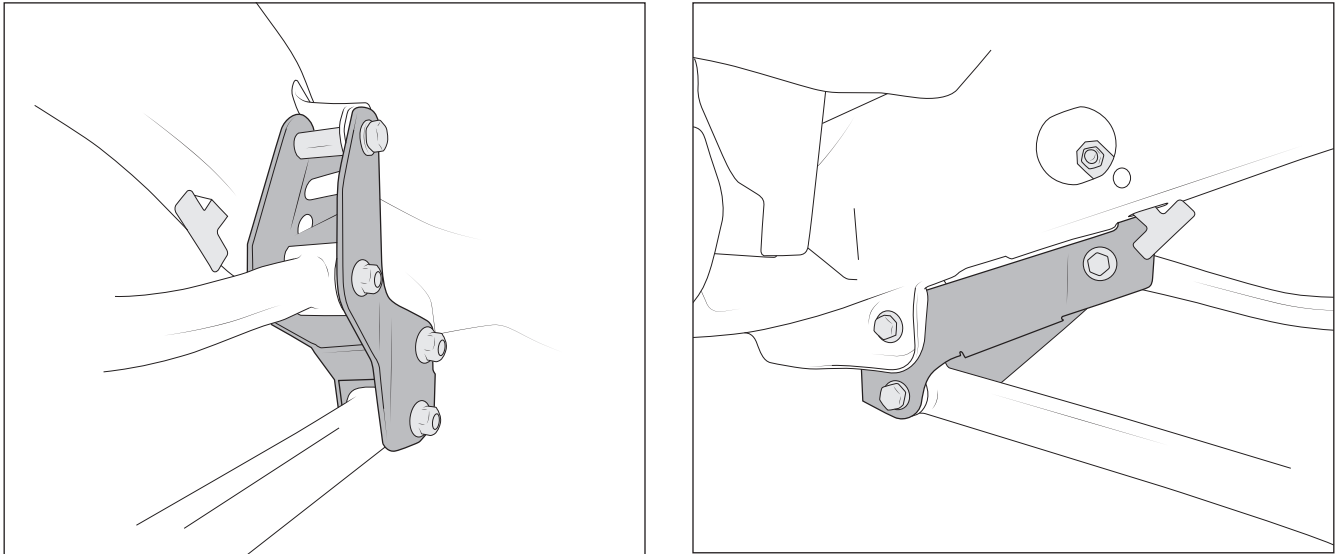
Innenansicht (links) Aussenansicht (rechts)
